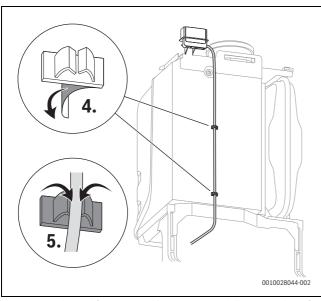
Applicare il fermacavi sul lato posteriore dell'apparecchio e fissare il cavo conduttore
